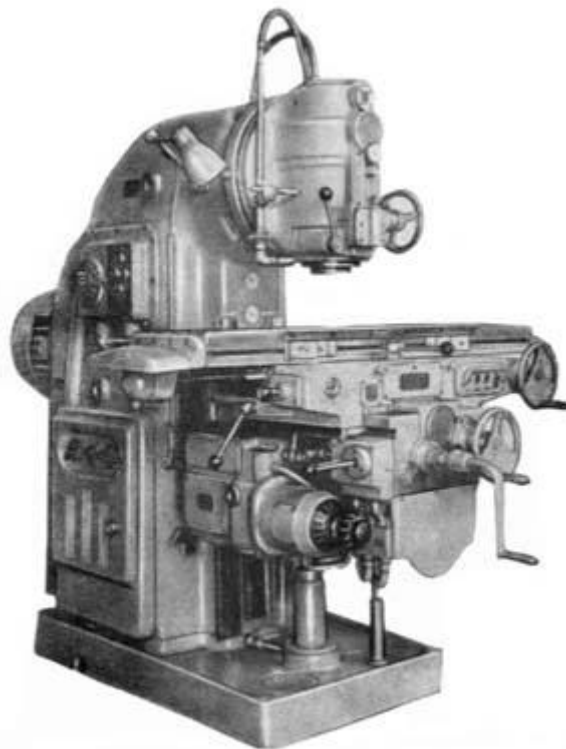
Вертикально-фрезерный станок 6М12П
